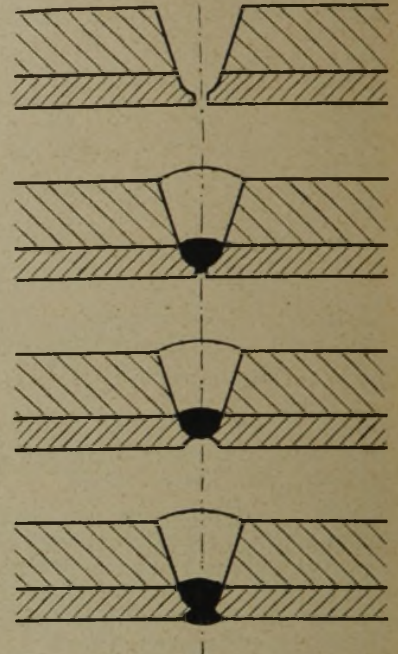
Schweißen von rostfrei plattierten Stahlblechen
